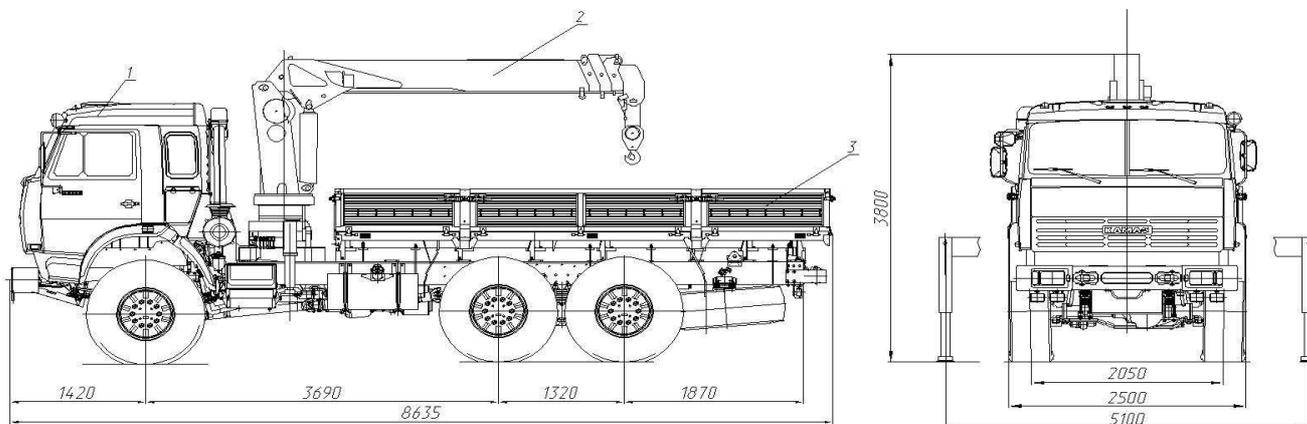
Общий вид 333801 на шасси КАМАЗ-43118-1050-10
